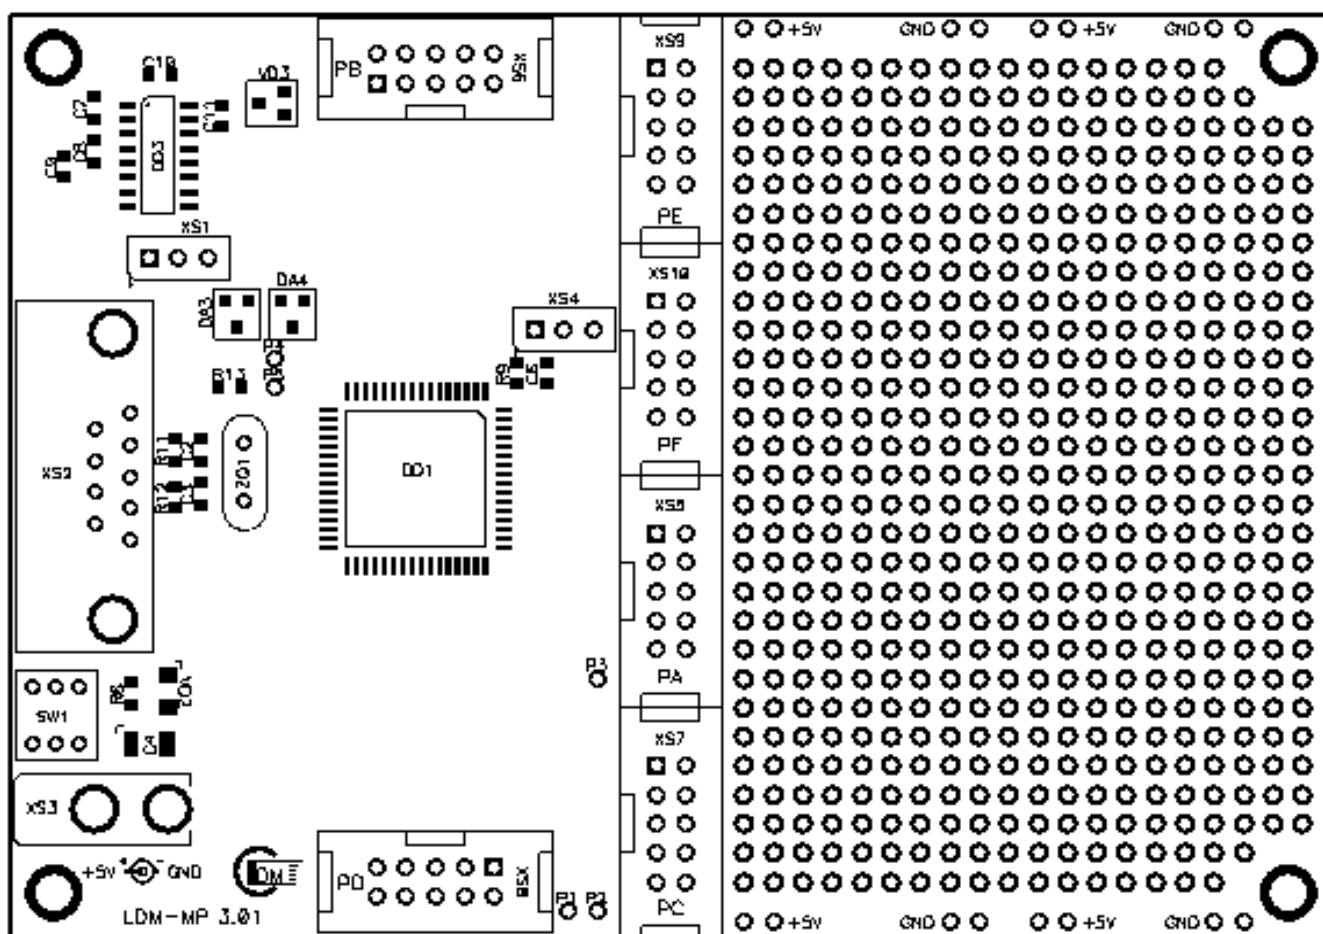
Внешний вид печатной платы контроллера-конструктора LDM-MP 3.01
